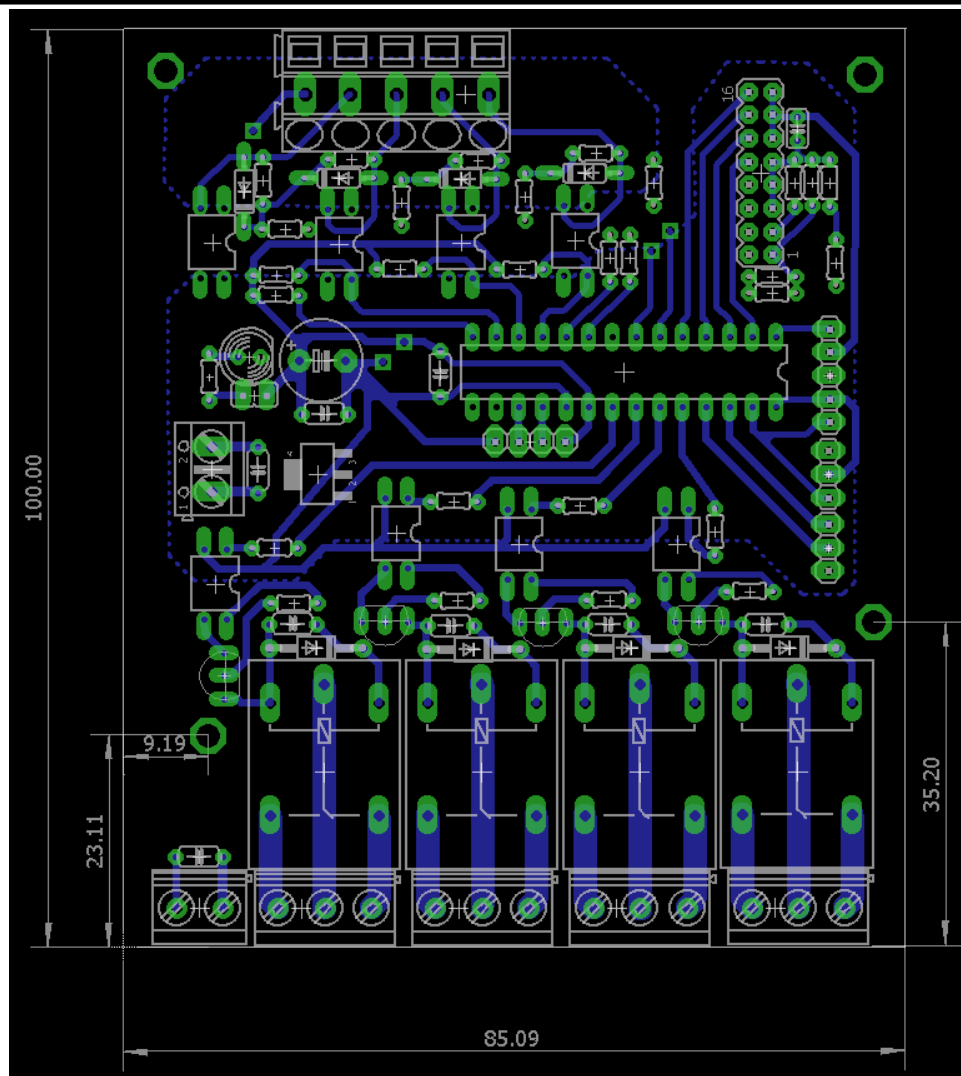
PCB Módulo Main – Bottom Layer.
